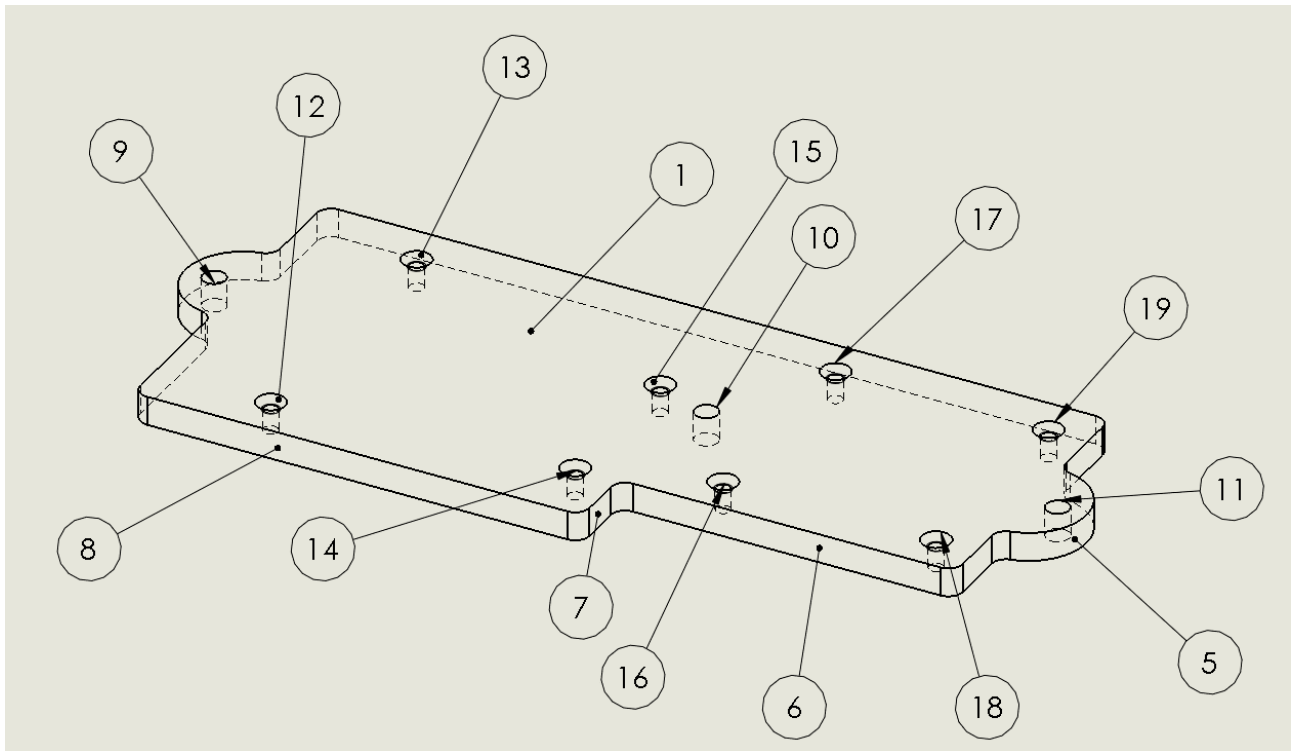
Креслення деталі з поверхнями із сторони закріплення плат керування
